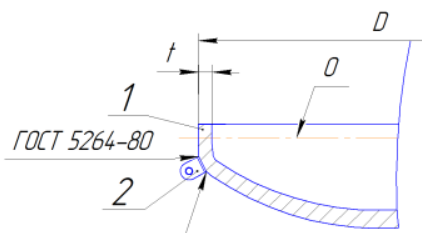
Схема приварки проушин к днищу. 1 – днище; 2 – проушина; O – большая ось эллипса; D – наружный диаметр днища; t – толщина стенки
